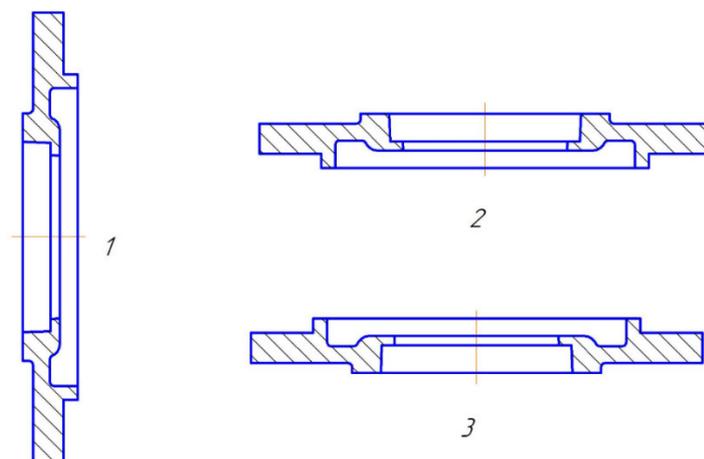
Возможные варианты расположения отливки в форме
